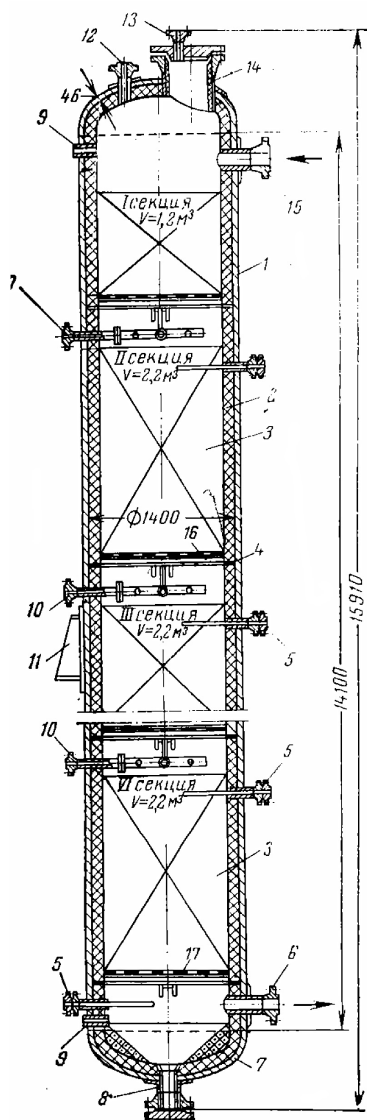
16. Политропический реактор установки гидроочистки дизельных топлив: 1 — корпус; 2 — футеровка; 3 — катализатор; 4 — опорное кольцо; 5 — штуцеры для термопары; 6 — вывод газосырьевой смеси; 7 — днище; 8 — нижний штуцер; 9 — муфта для манометра; 10 — опора; 11 — опора; 12 — штуцер для предохранительного клапана; 13 — воздушник; 14 — люк; 15 — штуцер ввода газосырьевой смеси; 16 — съемная колосниковая решетка; 17 — опорный перфорированный лист
